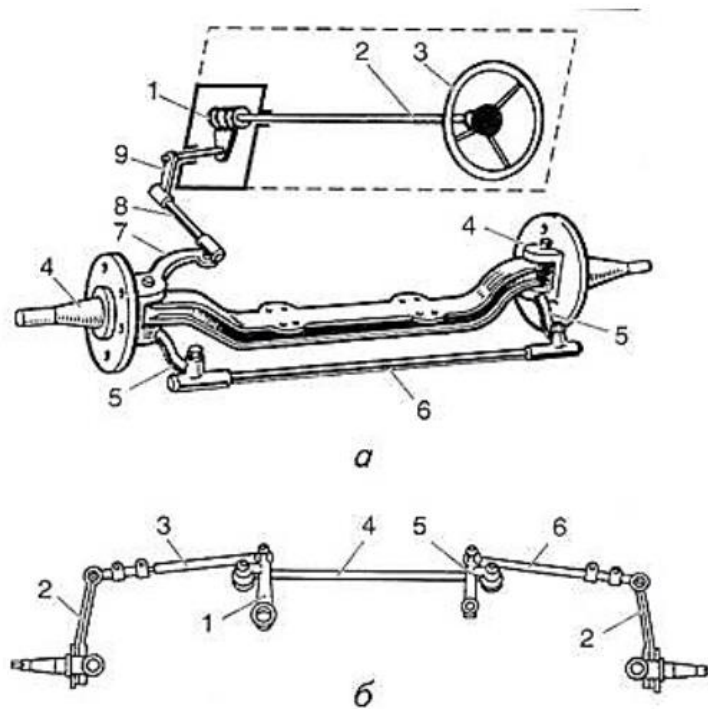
Схема рульового керування: а — залежна підвіска (1 — рульова передача; 2 — рульовий вал; 3 — рульове колесо; 4 — поворотна цапфа; 5 — нижні важелі лівої та правої поворотних цапф; 6 — поперечна тяга; 7 — верхній важіль лівої поворотної цапфи; 8 — поздовжня тяга; 9 — сошка рульового привода); б — незалежна підвіска (1 — сошка; 2 — поворотні важелі; 3, 6 — відповідно ліва й права бічні тяги; 4 — основна поперечна тяга; 5 — маятниковий важіль) [2].
